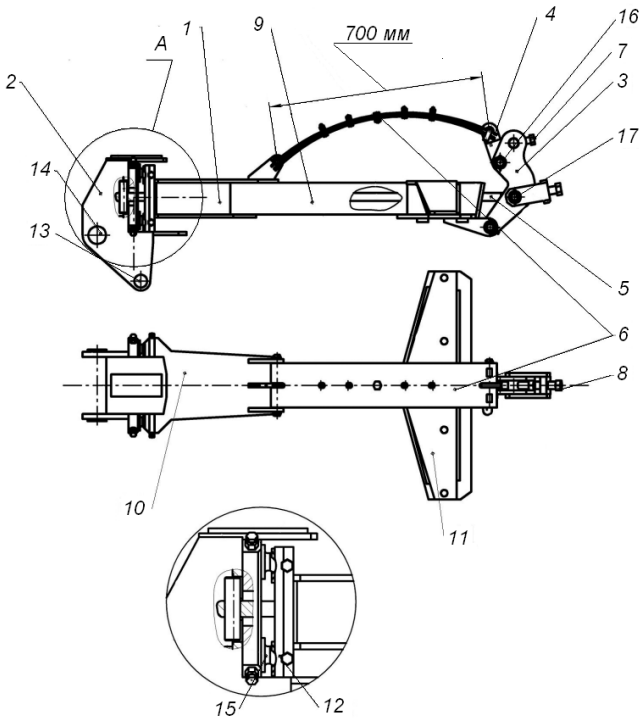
Предохранитель: 1 – грядиль; 2, 10, 11 – кронштейны; 3, 4 – рычаги; 5 – тяга; 6 – пластинчатая пружина; 7, 8 – регулировочные болты; 9 – труба; 12 – упоры; 13, 14 – болты; 15 – цапфы; 16, 17 – оси
